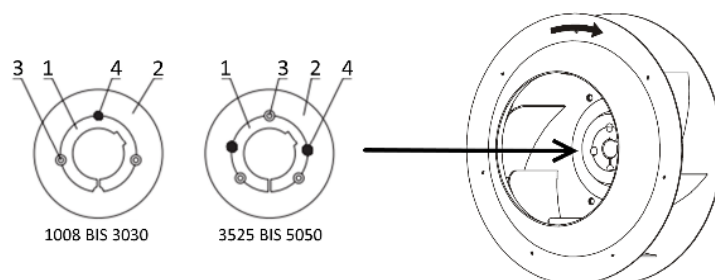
Схема установки крыльчатки с зажимной втулочной ступицей.
